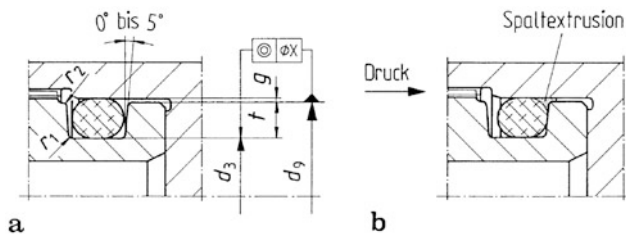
O-Ring mit Einbauräum außen dichtend als Deckeldichtung. a Nach dem Einbau mit Maßen des Einbauräum, Anwendungsfall: Hydraulik, ruhend, DIN ISO 7425 Teil 1; b unter Druck
